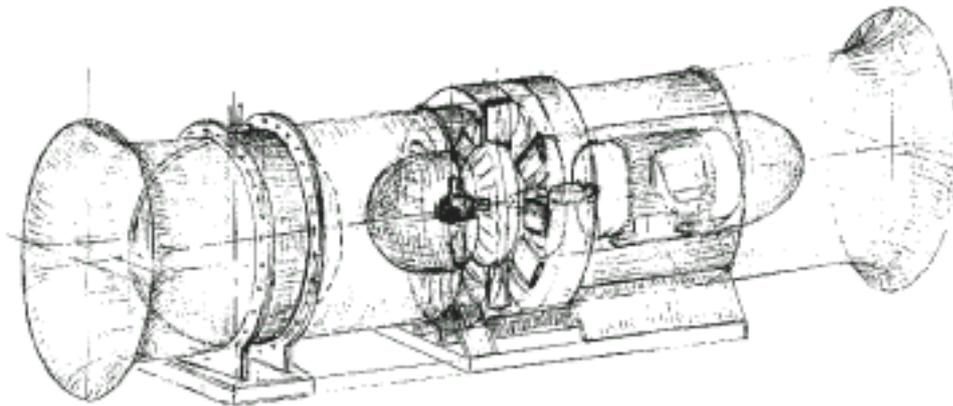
Esquema do conjunto turbina - gerador [9].
